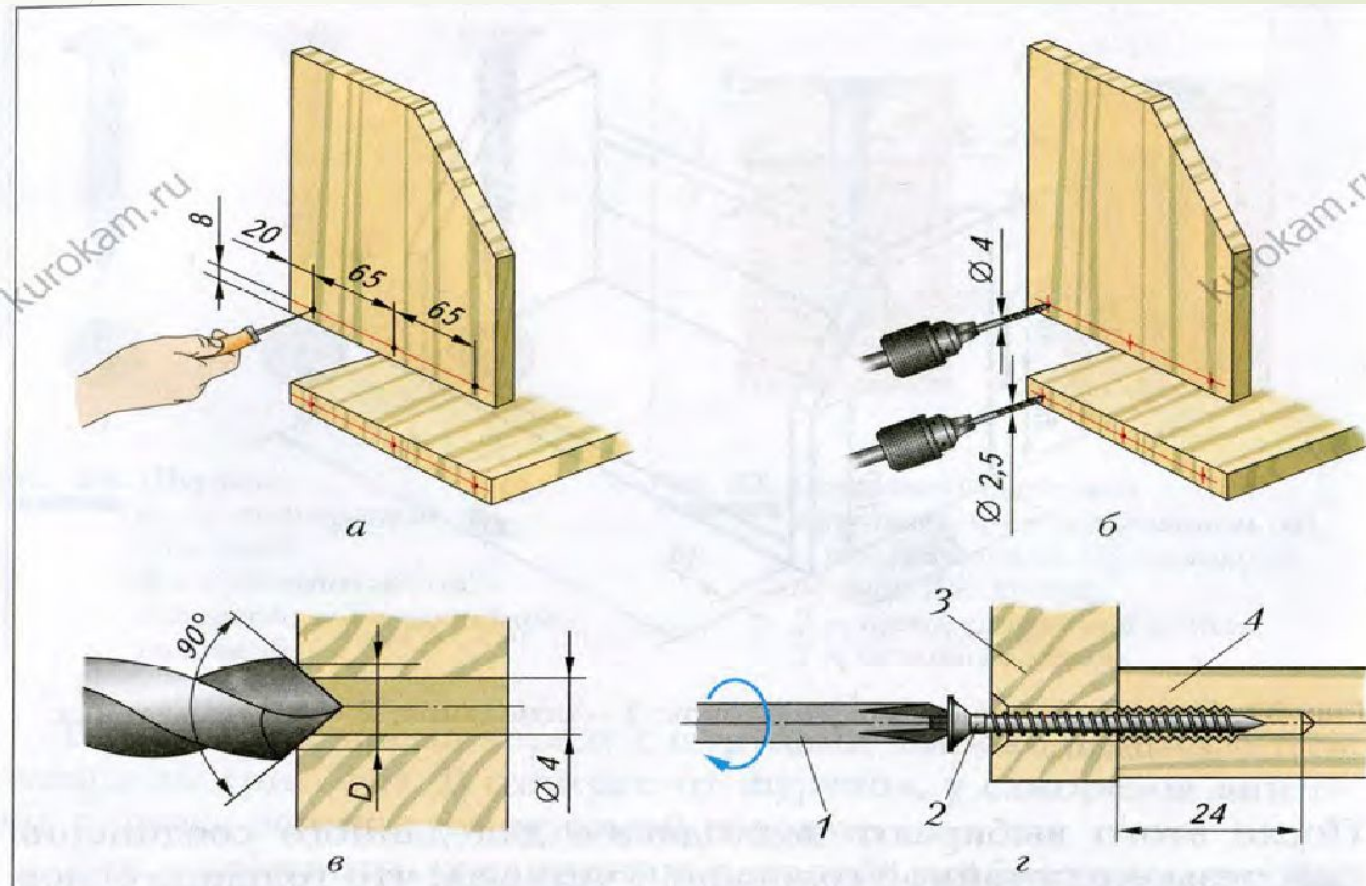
Последовательность соединения боковой стенки с основанием настольной полки: а – разметка; б – сверление отверстий под саморезы; в – выполнение фаски у сквозного отверстия; г – ввинчивание самореза: 1 – отвёртка; 2 – саморез; 3 – боковая стенка; 4 – основание
